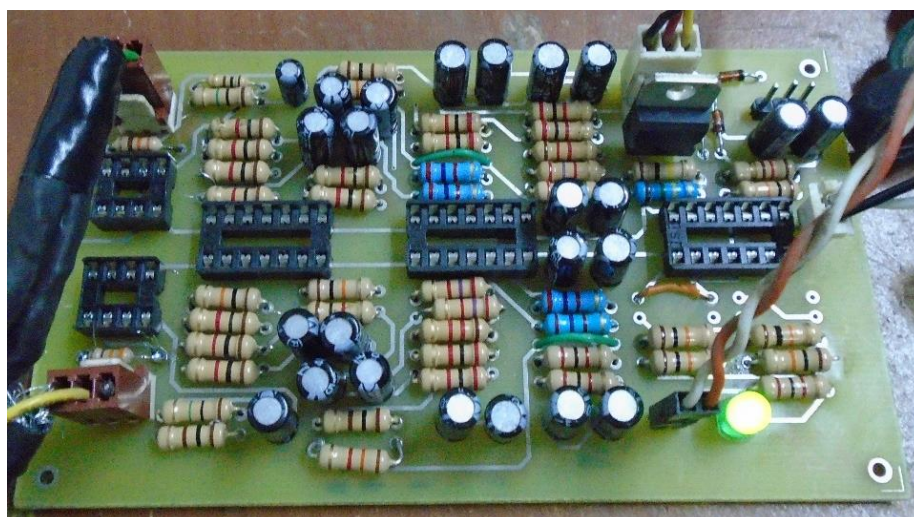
PCB del circuito de acondicionamiento soldado
